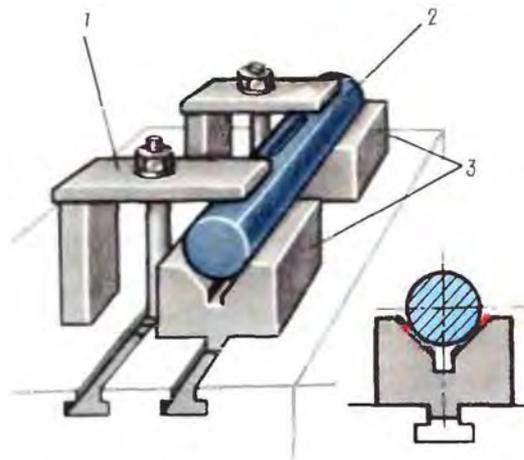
Установка вала при фрезеровании шпоночного паза
